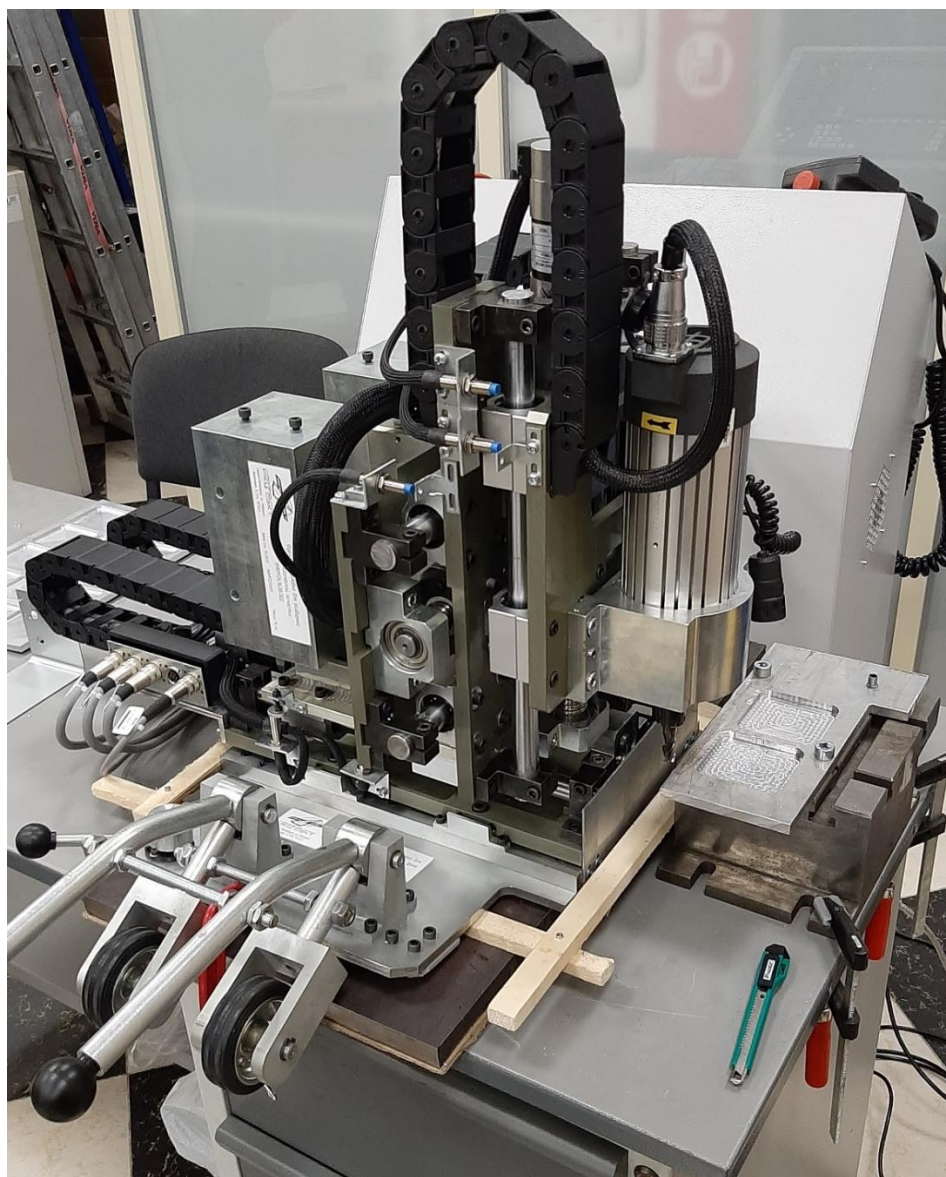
Внешний вид фрезерного станка в сборе
